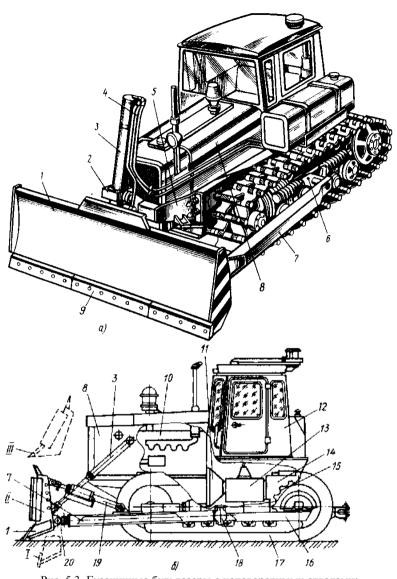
Гусеничные бульдозеры с неповоротными отвалами: а – с жесткими толкающими брусьями, б – с шарнирными брусьями; 1 – отвал; 2 – несущая рамка; 3 – гидроцилиндр подъема/опускания отвала; 4 – рукав; 5 – подрамник; 6 – поперечная балка; 7 – толкающий брус; 8 – трактор; 9 – нож; 10 – двигатель; 11 – муфта сцепления; 12 – кабина; 13 – коробка передач; 14 – задний мост; 15 – звездочка; 16 – гусеничная тележка; 17 – гусеница; 18 – шарнир; 19 – гидрораскос; 20 – универсальный шарнир; 1 – нижнее положение отвала, II – рабочее, III – транспортное
